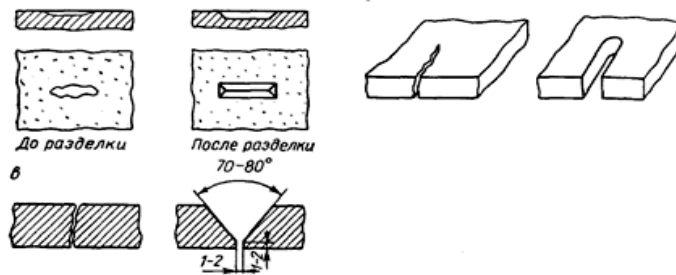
Схема подготовки дефекта к сварке:
